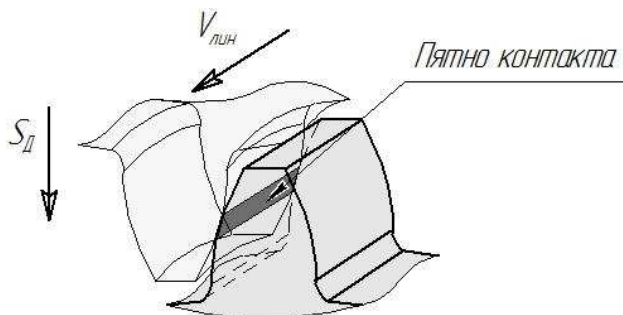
Схема касания поверхностей обрабатываемого зуба колеса и зуба притира
